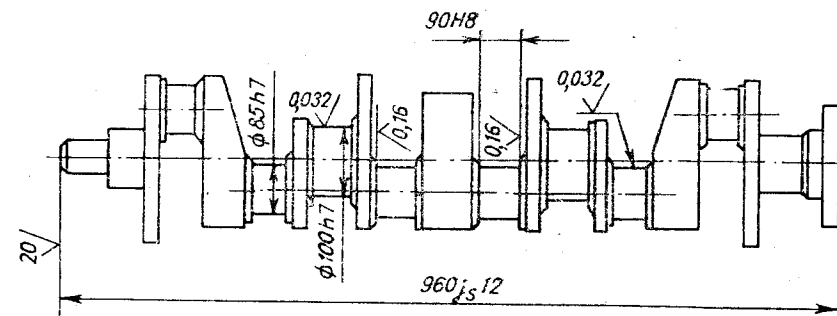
Колінчастий вал автомобільного двигуна внутрішнього згорання.
